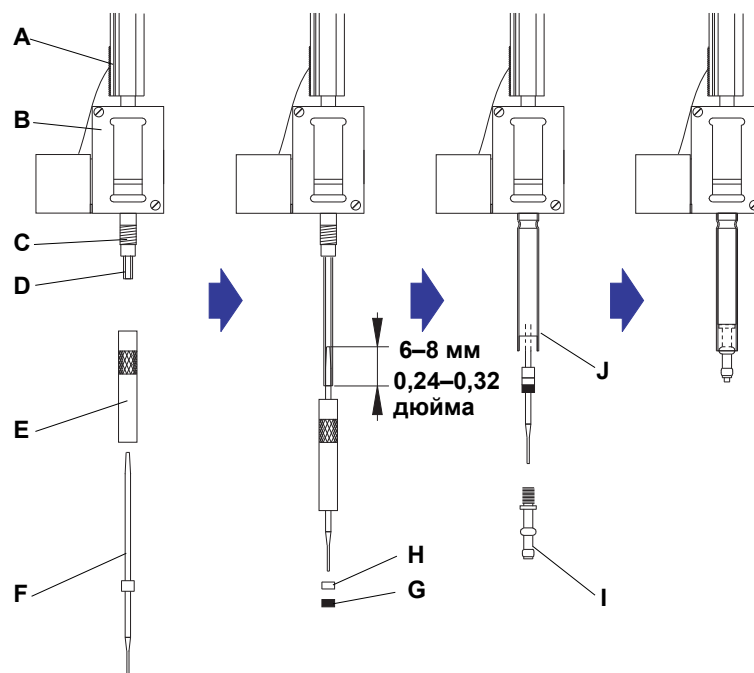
Установка механизма захвата одноразовых наконечников
